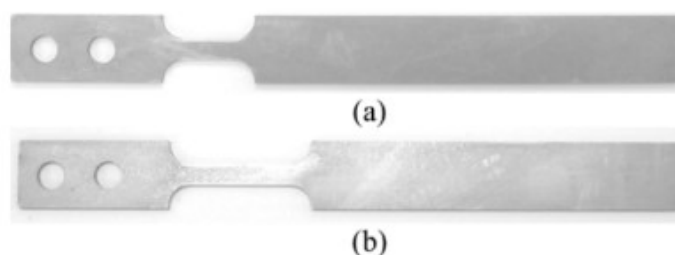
Corpos de prova com 15 e 30 mm de comprimento útil
